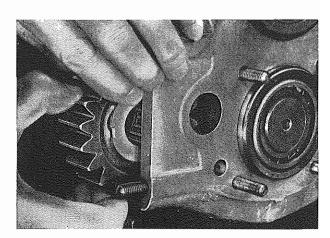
Ingranaggio della retromarcia Reverse gear
